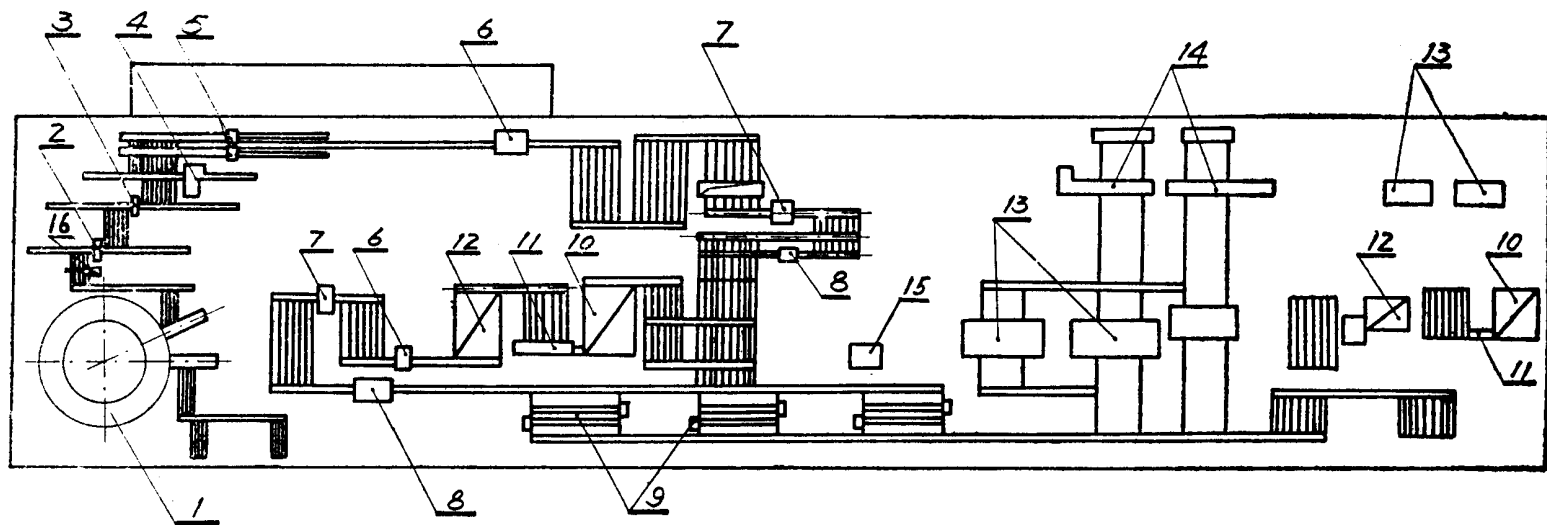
日本钢管京浜厂 16" 自动轧管机组平面布置图
